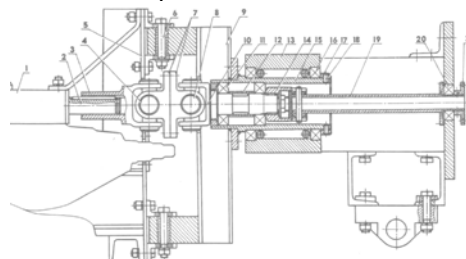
Механізм керування міні-трактором: 5 – напірвма передня; 6 - вісь шарніру вертикальної осі; 9 – напірвма задня, 13 – корпус підшипникового вузла.
